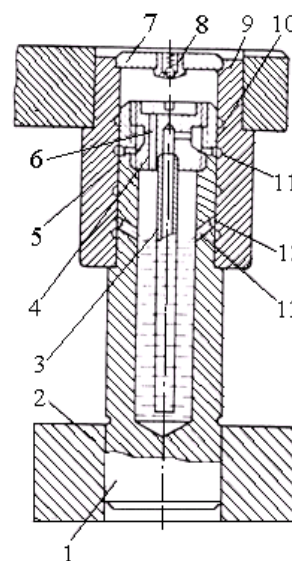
Конструкция направляющих элементов штампа с принудительной подачей смазки
